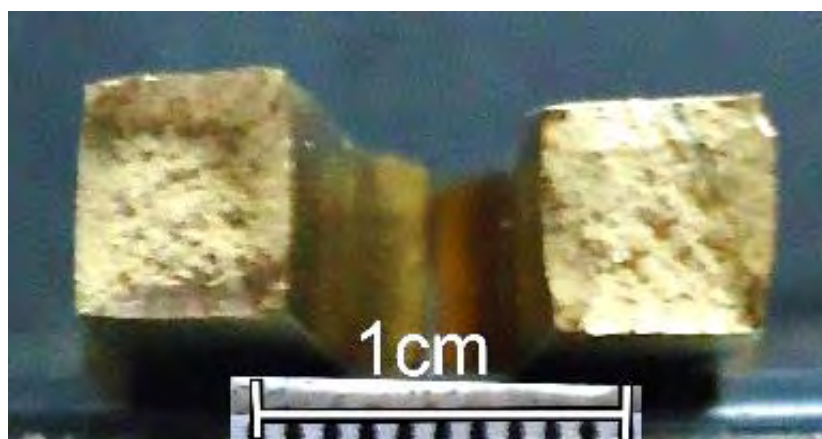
Fractura de la probeta de tensión de latón en molde de cobre
